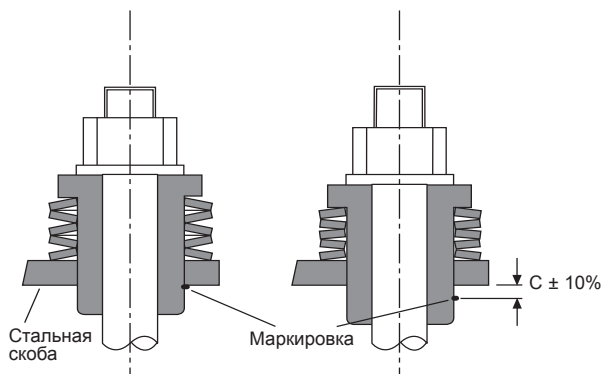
Регулировка предварительного сжатия дисковых пружин
